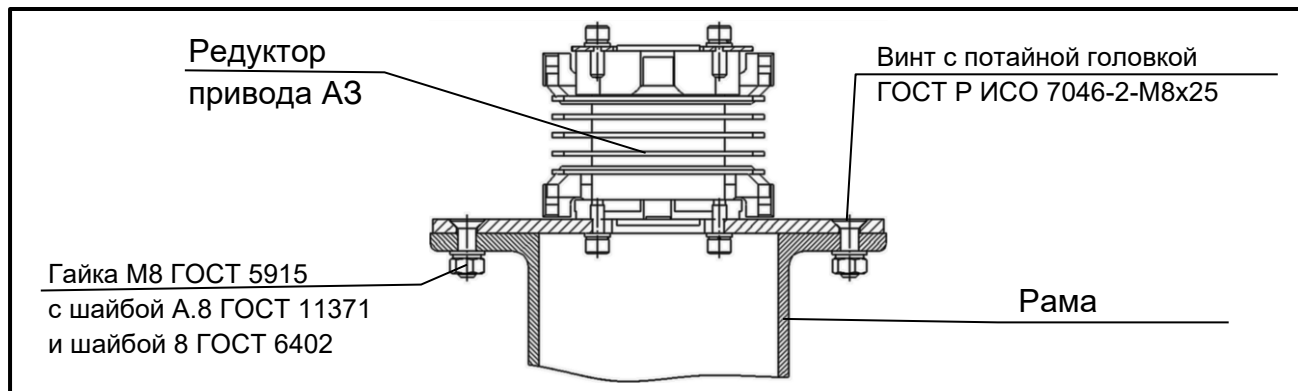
Установка сборки основания, волнового редуктора, рамы и привода АЗ (кабели условно не показаны)
